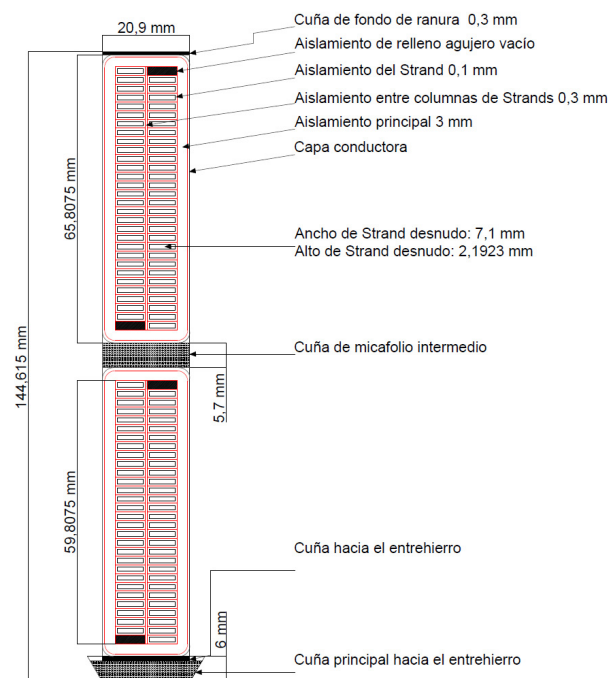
Dimensiones del método Juan Corrales. Fuente: [5]
